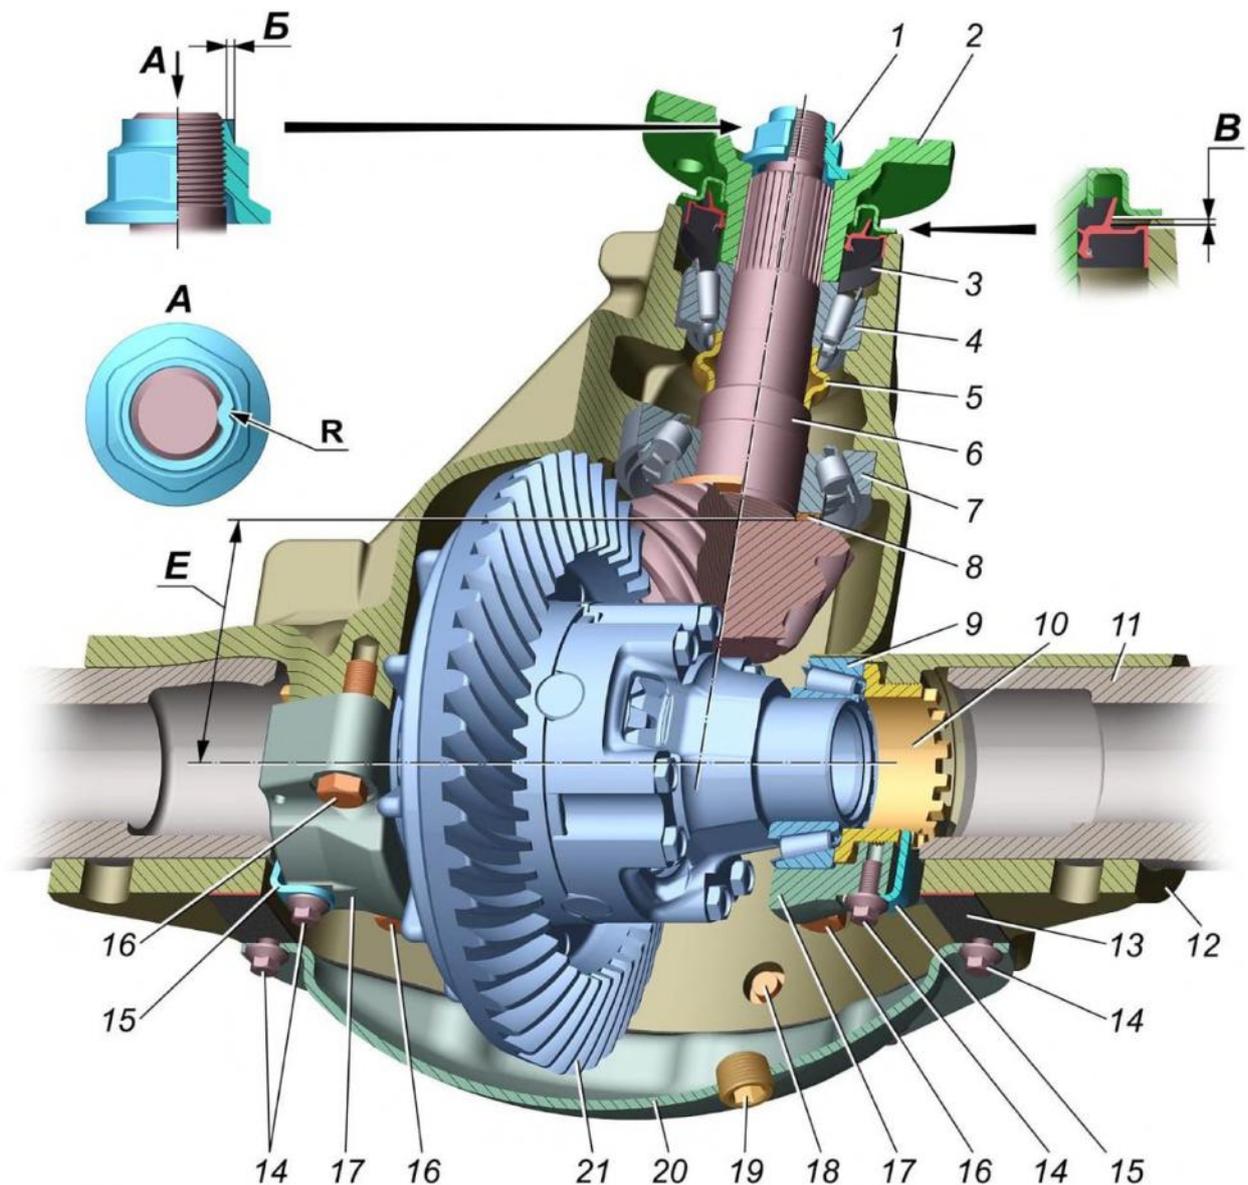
Редуктор заднего моста с кожухами полуосей: 1 - гайка; 2 - фланец ведущей шестерни; 3 - манжета; 4,7,9 - подшипники; 5 - распорная втулка; 6 - ведущая шестерня; 8 - регулировочное кольцо; 10 - гайка подшипников дифференциала; 11 кожух полуоси; 12 - картер заднего моста; 13- прокладка; 14,16 – болты; 15 - стопорная пластина; 17 - крышка подшипника дифференциала; 18- пробка магнитная; 19 - пробка маслозаливного отверстия; 20 – крышка картера; 21 – дифференциал с ведомой шестерней
